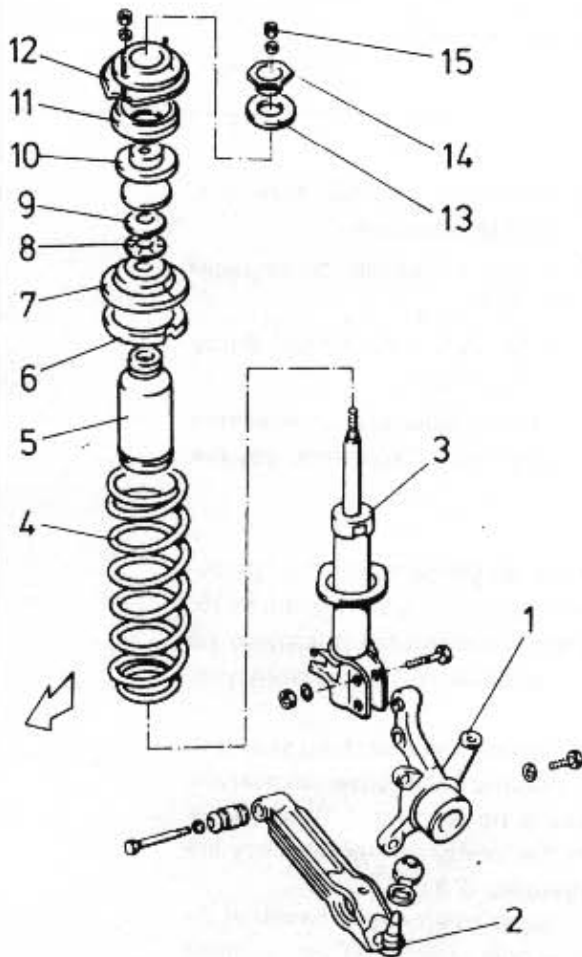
ODŁĄCZANIE KOLUMNY ZAWIESZENIA OD ZWROTNICY
